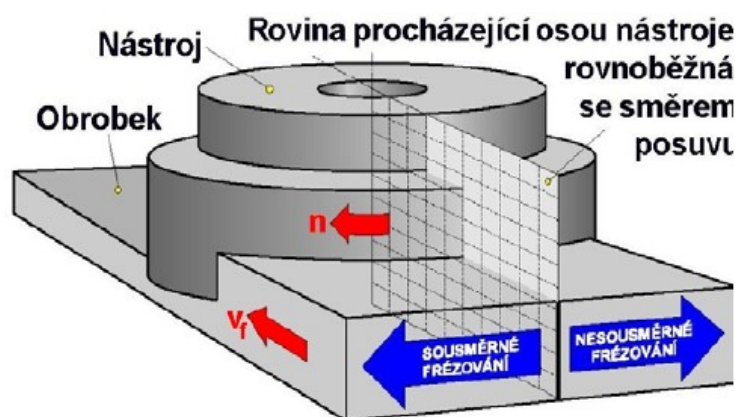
Pohyb nástroje a obrobku - sousledné frézování [2]
